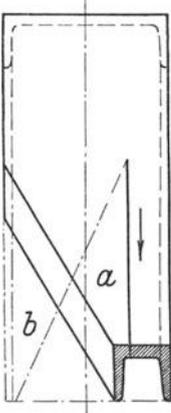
Profilverjüngung durch Schweißen.
